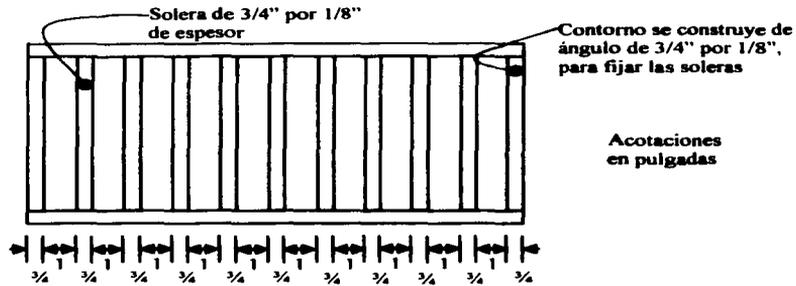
Rejilla tipo Irving, construida en acero inoxidable.
